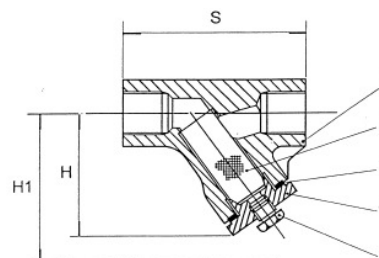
Y-Filter mit NPT- oder Schweißmuffe
